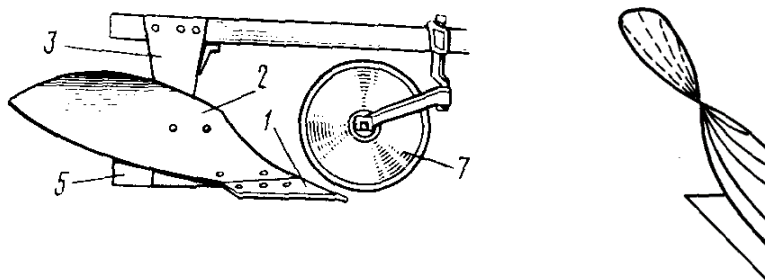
Схема корпуса с отвалом винтового типа
